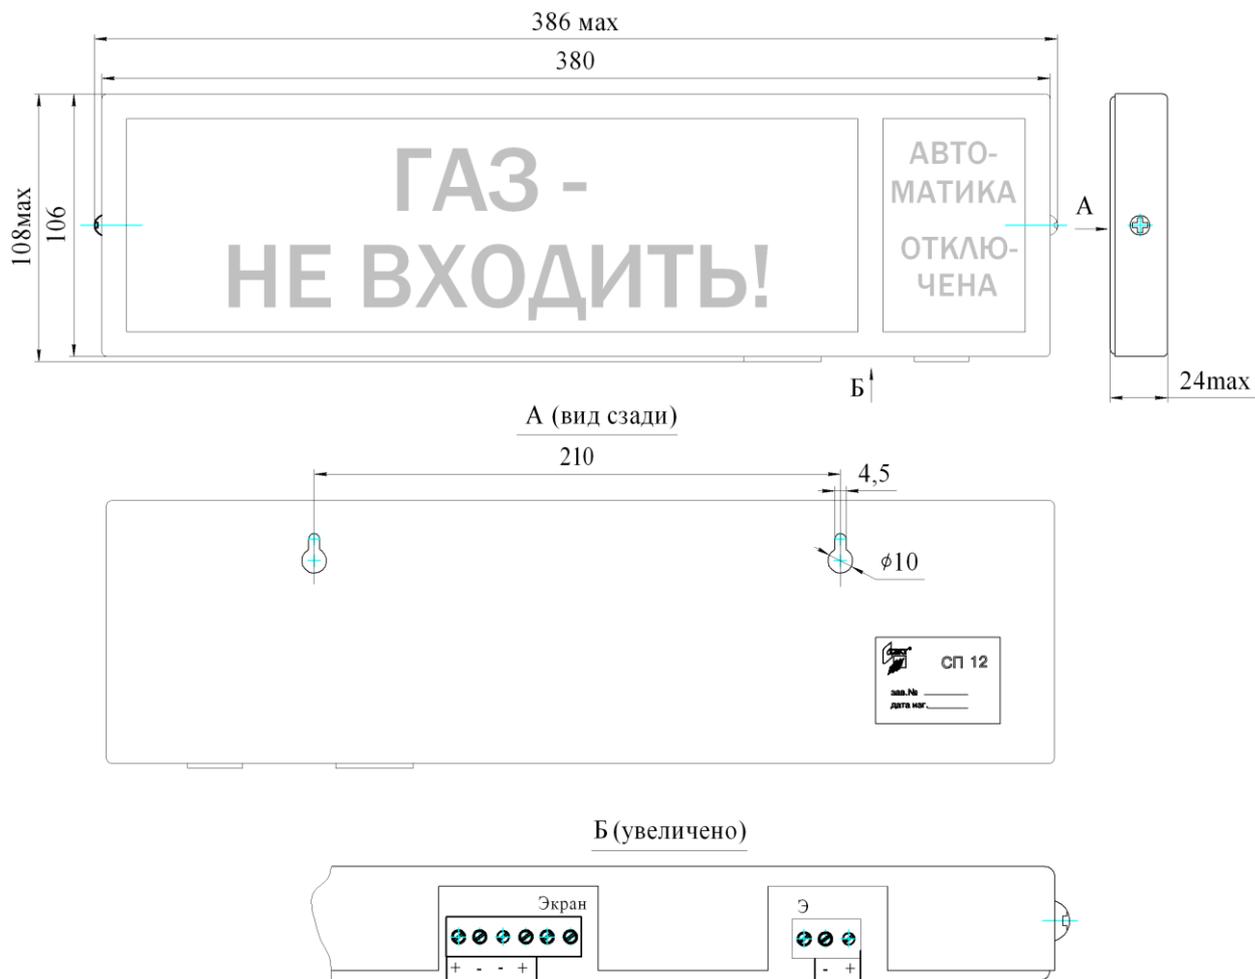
Оповещатель двойной СП 12. Габаритный чертёж
